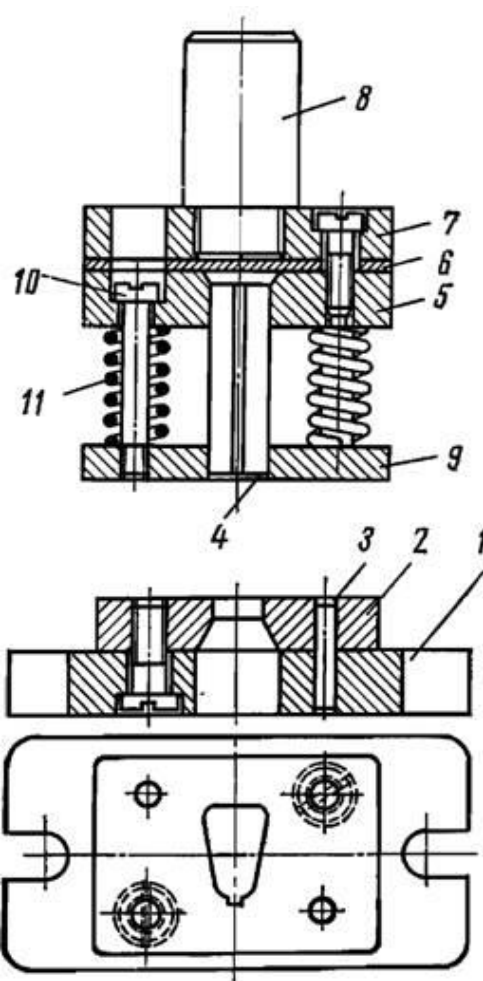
Пазовый штамп для пробивки пазов в листе статора
